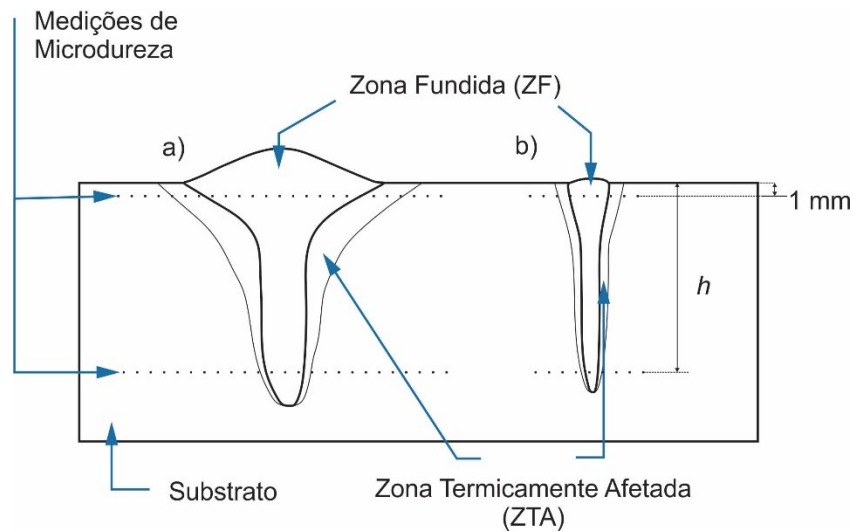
Esquemático das regiões de medição de microdureza nas seções transversais das amostras soldadas pelos processos de soldagem a) HLAW, e b) LBW. (Fonte: Autor)
